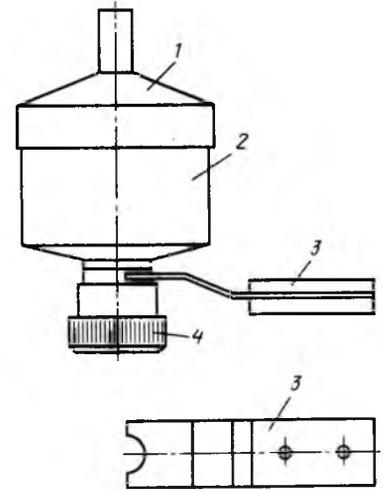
1 — крышка; 2 — корпус; 3 — «вилка».
